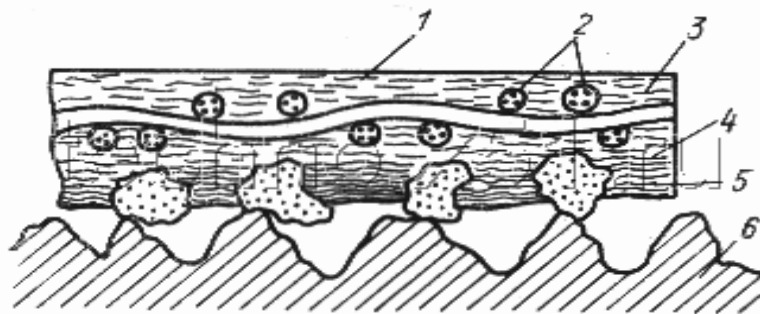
Схема процесу оброблення абразивною стрічкою:
